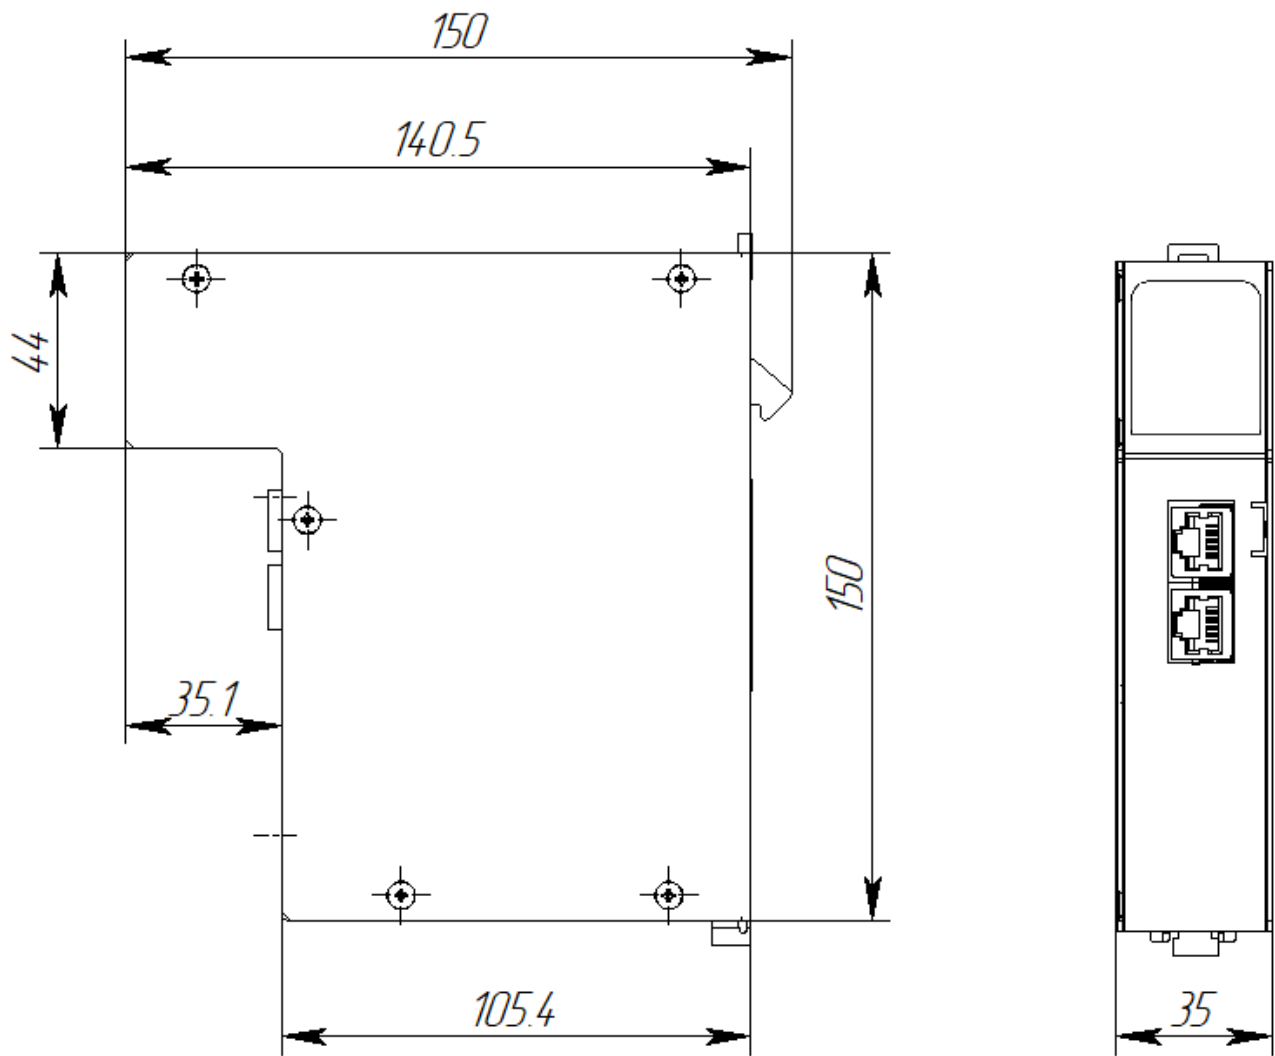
Габаритные и присоединительные размеры модуля коммуникационного с интерфейсом Ethernet в металлическом корпусе
